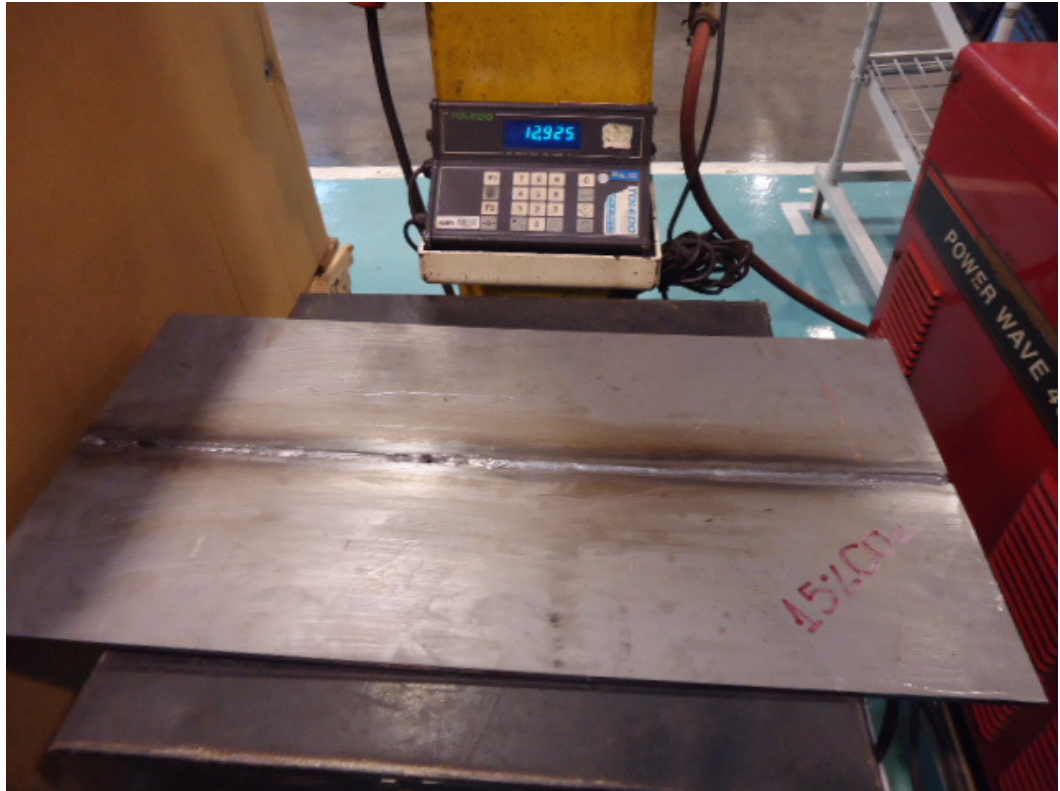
Chapa após a soldagem com mistura 15% CO_2
